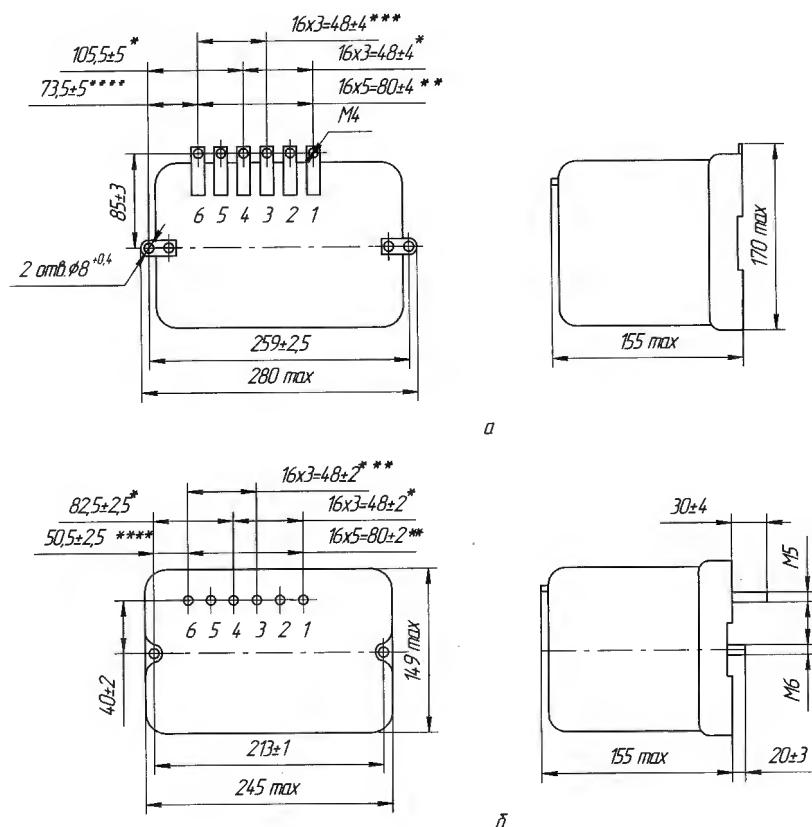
Габаритные, установочные, присоединительные размеры реле серии РТ 80, РТ 90:
